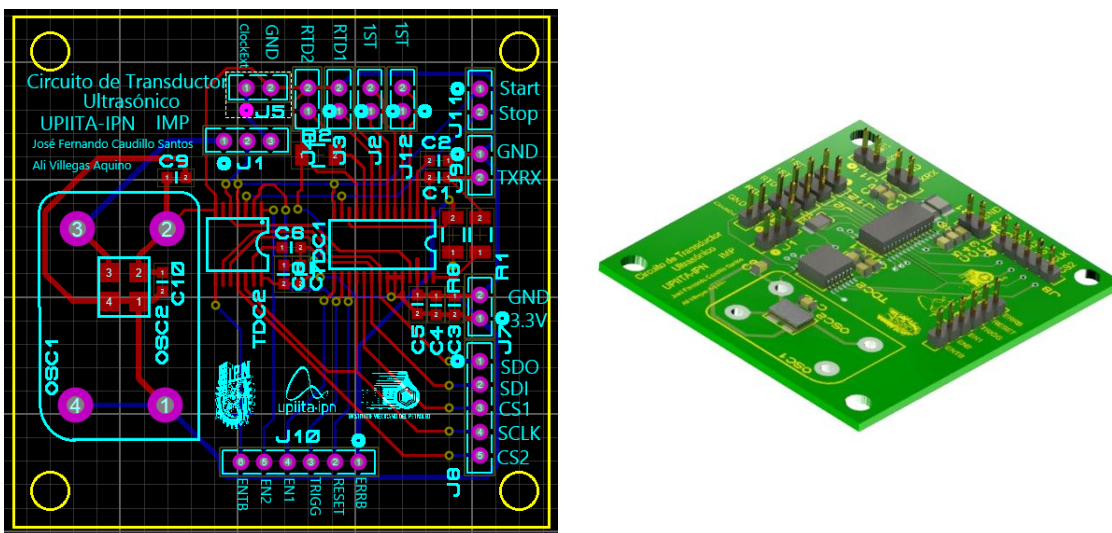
Diseño del PCB y Modelo en 3D del circuito de transductor ultrasónico
